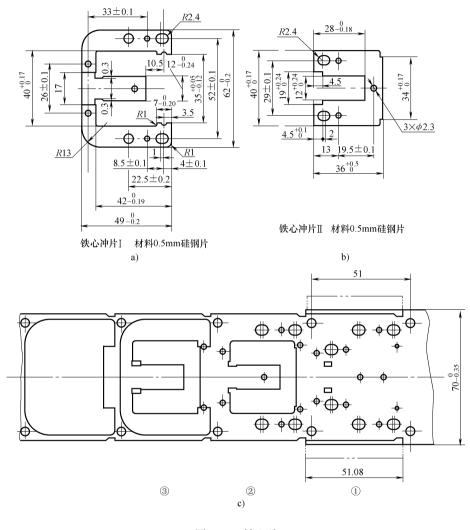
铁心片 a)、b) 零件图 c) 排样图
